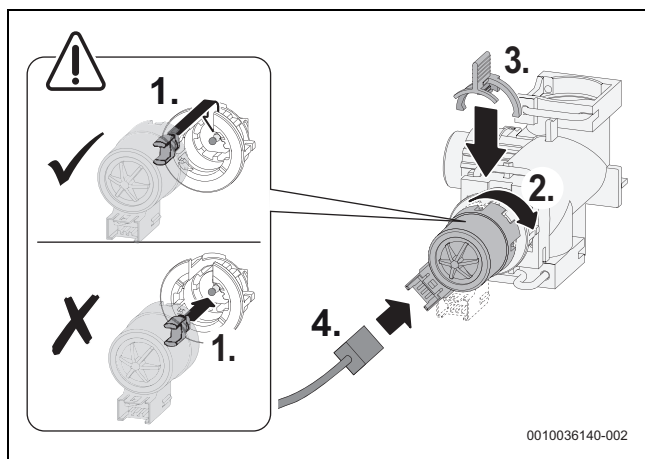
Instalar el motor en la válvula de 3 vías (variante sin tornillos)
